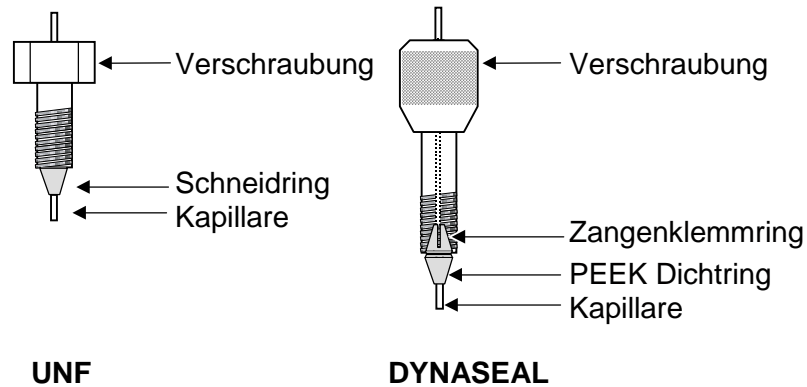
Prinzip der UNF- und DYNASEAL-Verschraubungen
